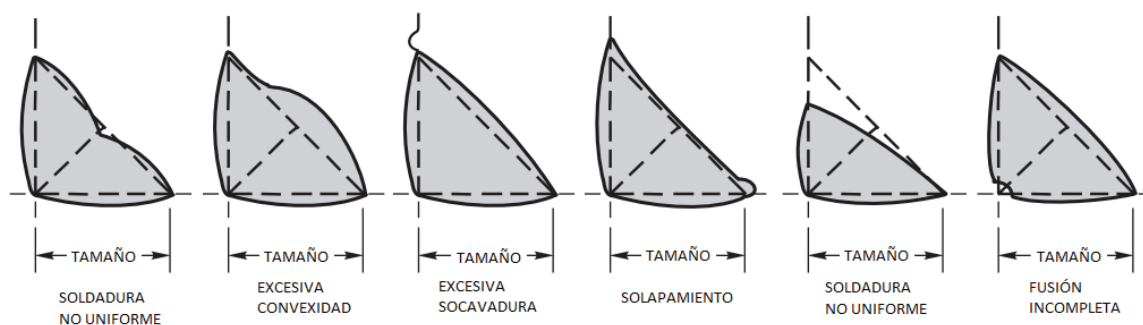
Perfiles de soldadura inaceptables.
